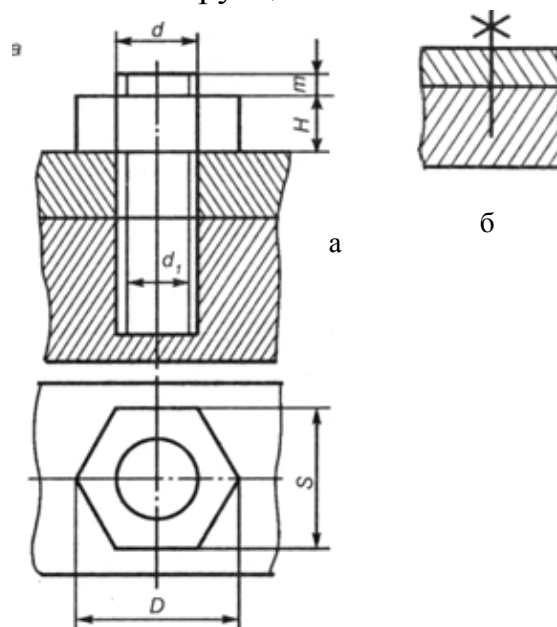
Условное изображение соединения шпилькой и соотношения размеров деталей
